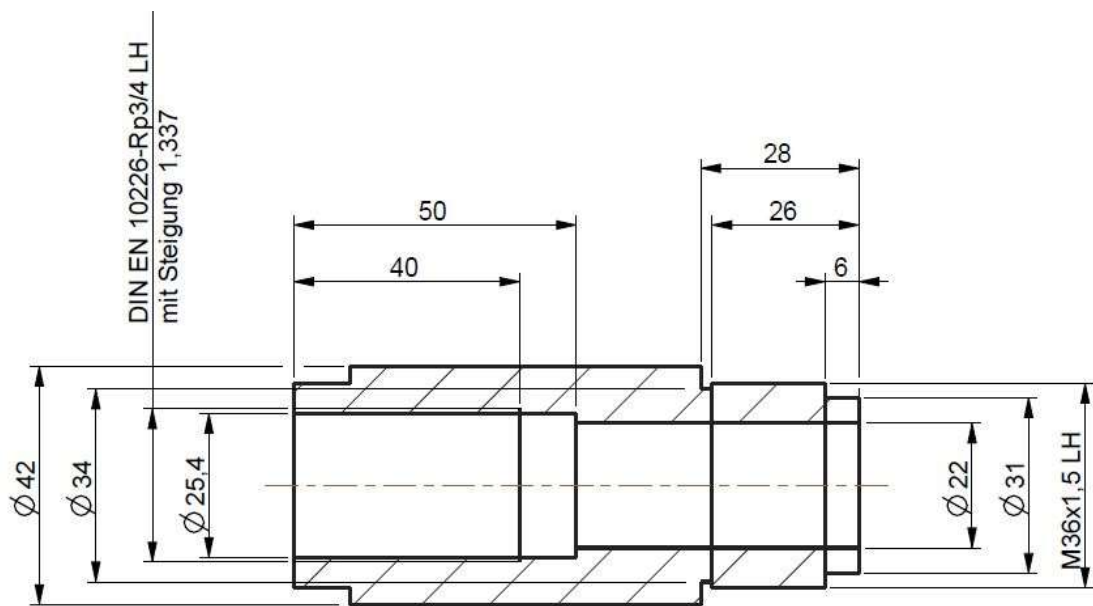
Konstruktionszeichnung des Adapters – Schnittansicht
